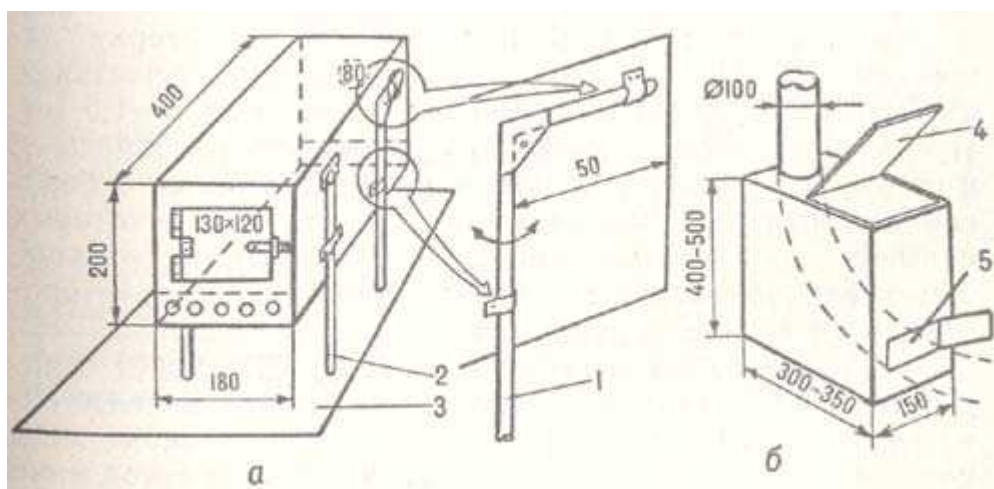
Смонтированные печи: а — с горизонтальной, б — с вертикальной загрузкой дров. 1,2 — поворачивающиеся и вынимающиеся ножки; 3 — металлическая (асбестовая) Подставка под печку; 4 — крышка; 5 — поддувало
